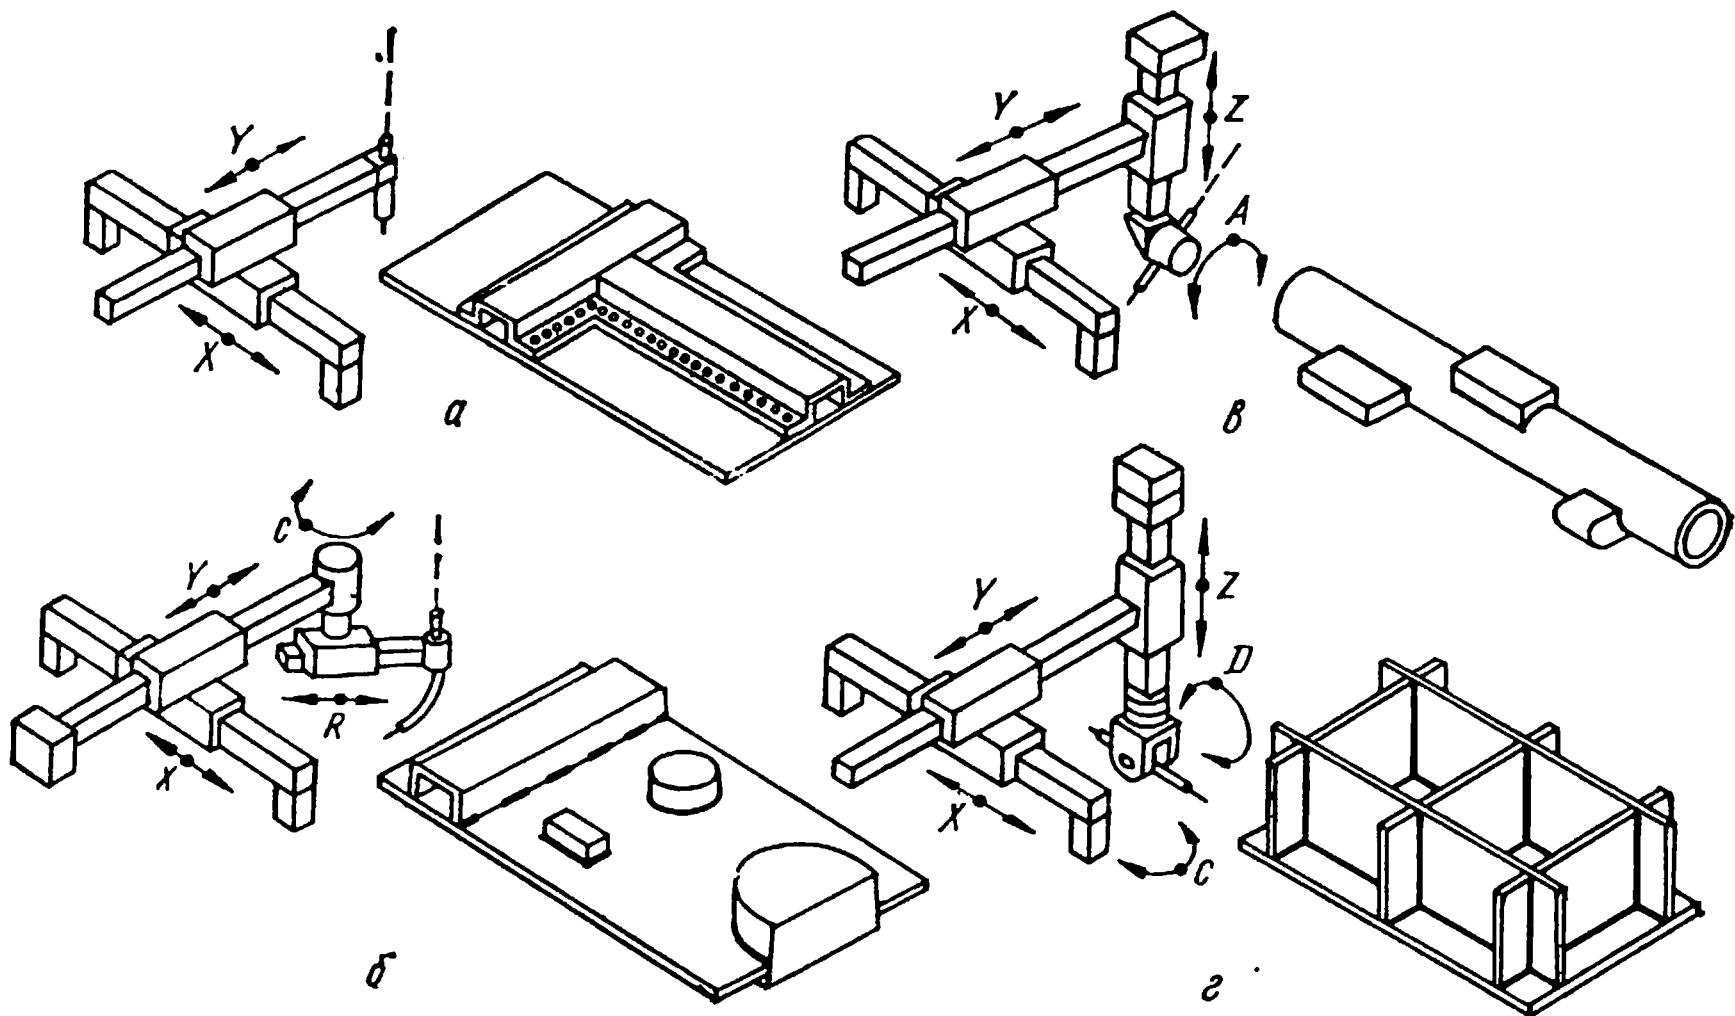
Компонентные схемы специализированных манипуляторов сварочного инструмента и фрагменты типовых изделий при цикловом управлении координатами
